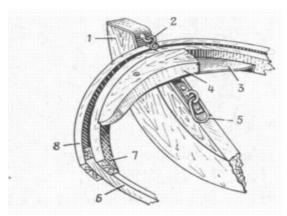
Крепление привальных брусьев: 1 — форштевень; 2 — гак для крепления кливер-галса; 3 — стальная кница; 4 — деревянная накладка (брештук); 5 — носовой рым; 6 — шпангоут; 7 — привальный брус; 8 — ширстрек
